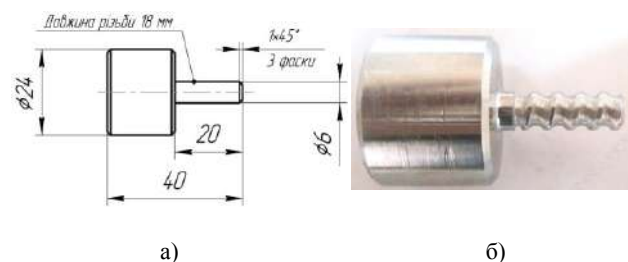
Металева вставка круглої зовнішньої різьби: а – ескіз металевої вставки; б – фото вставки
